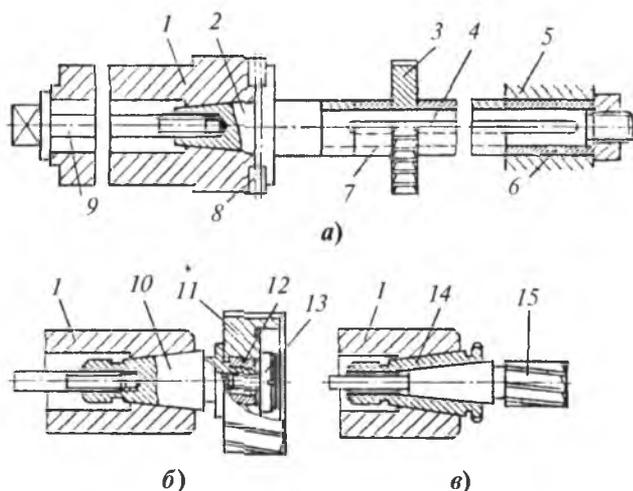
Схемы установки и закрепления фрез на станке:
